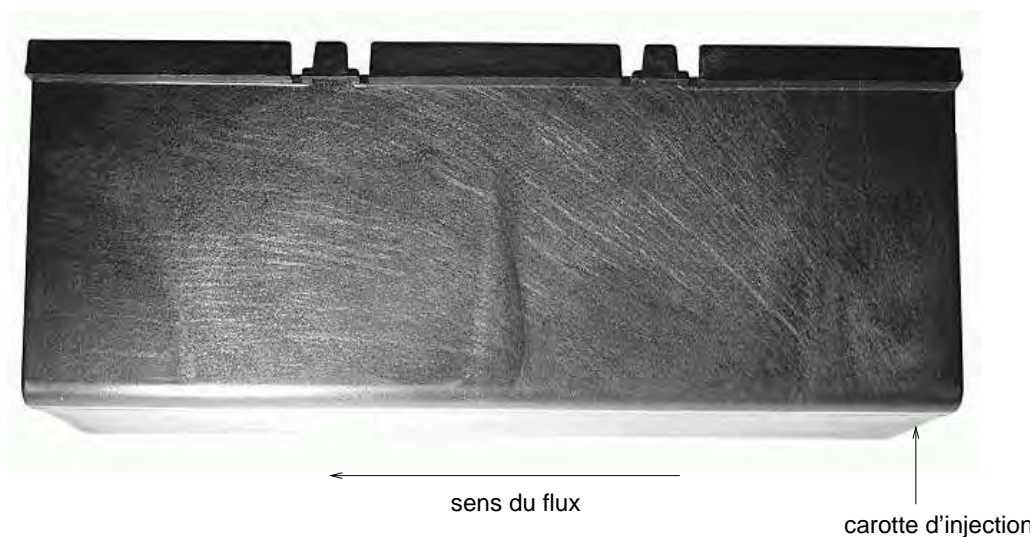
Photographie du flanc de la traverse (injection par la droite)
